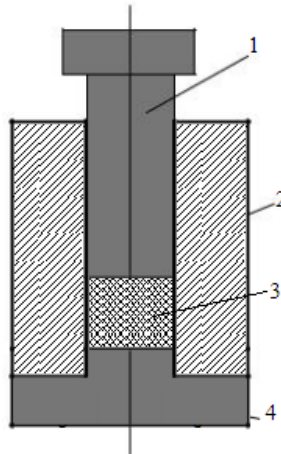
Схема пресс-формы для одностороннего холодного прессования порошков: 1 – пуансон верхний; 2 – матрица; 3 – порошок; 4 – пуансон нижний (неподвижный)
